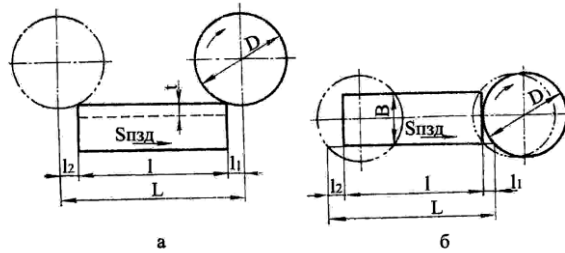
Схема визначення розрахункової довжини заготовки при фрезеруванні циліндричною (а) і торцевою (б) фрезами
